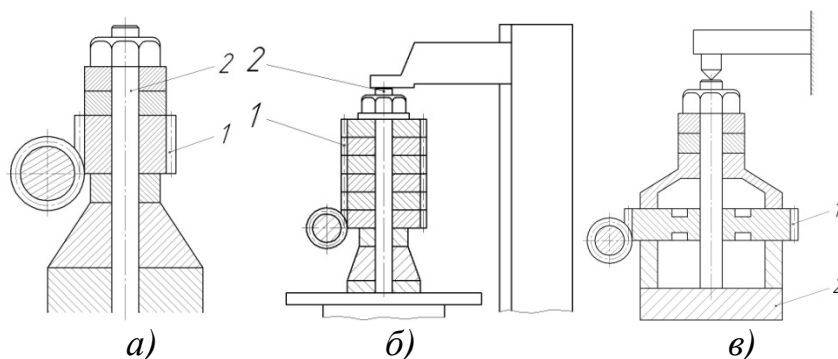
Типовые способы крепления заготовок на зубофрезерных станках
